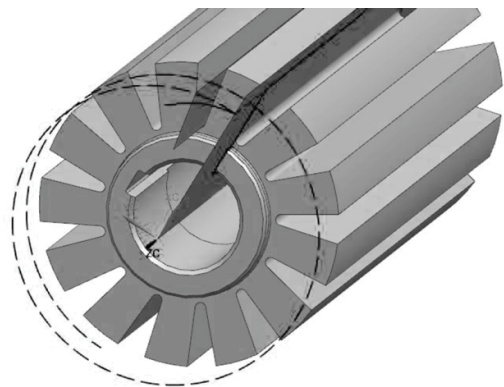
Заготовка червячной фрезы с нарезанными стружечными канавками
